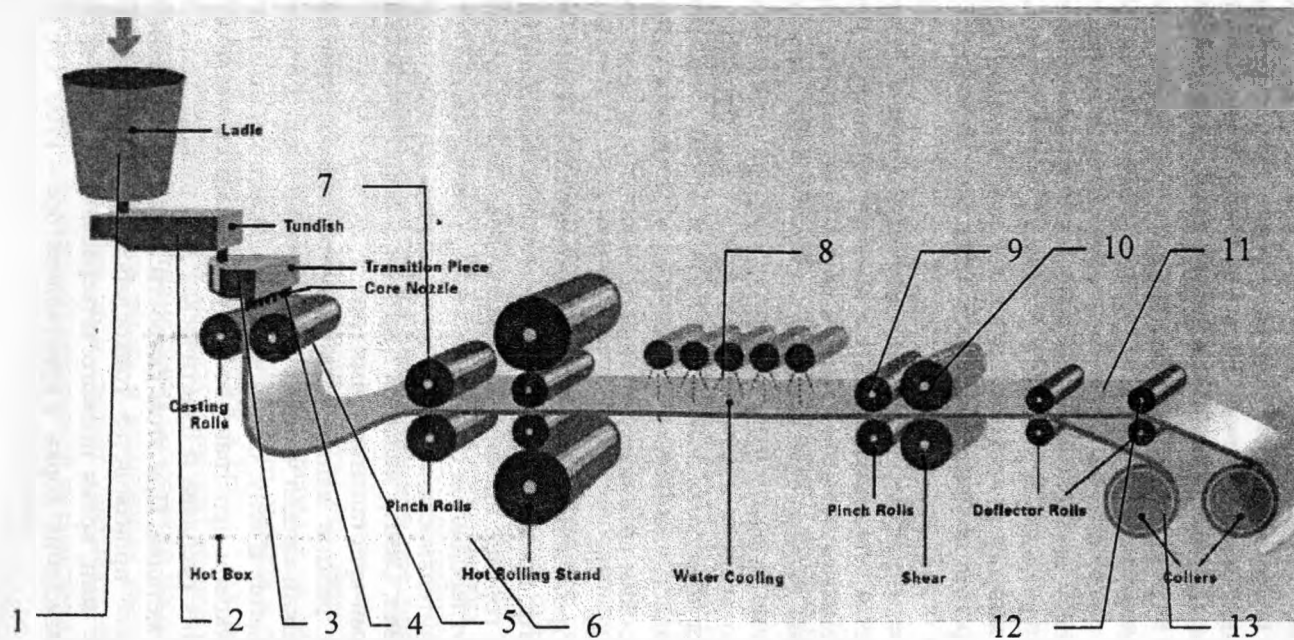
Схема процесса Castrip: 1 – ковш; 2 – промежуточный ковш; 3 – распределитель жидкого металла; 4 – форсунки; 5 – валки-кристаллизаторы; 6 – камера с инертным газом (тепловой бокс); 7 – прокатный стан; 8 – зона охлаждения; 9, 10 – захватывающие ролики; 11 – зона разрезки; 12 – отклоняющие ролики; 13 – наматывающие устройства
